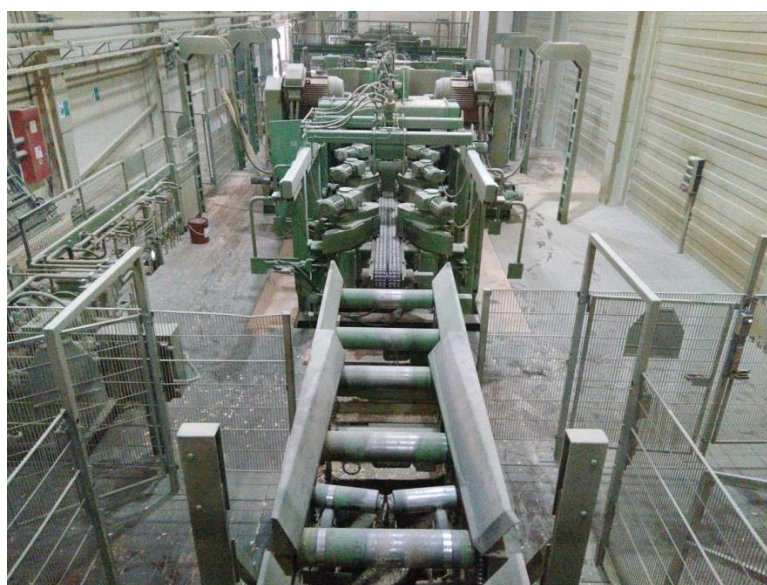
Фрезерно-профилирующая линия "LINCK"
